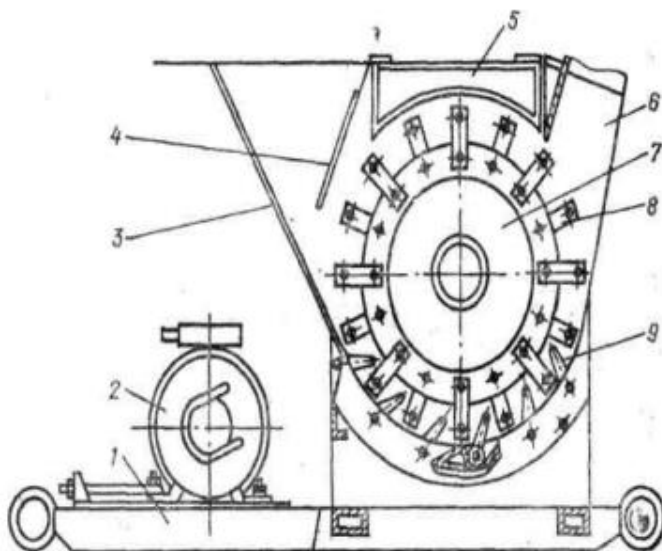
Структурна схема подрібнювача ИРМ-50: 1 – рама; 2 – електропривод; 3 – завантажувальна горловина; 4 – заслінка; 5 – кришка; 6 – розвантажувальний кормо привід; 7 – барабан; 8 – молоток (ніж); 9 – дека з ножами.
